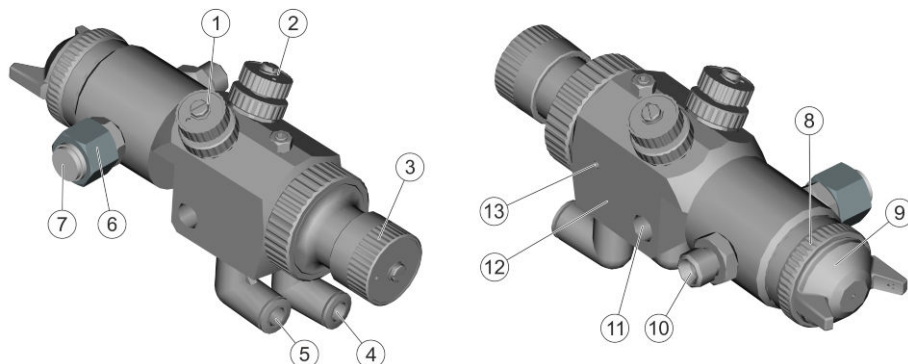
Aperçu du produit (variante du pistolet d'injection ACV)
